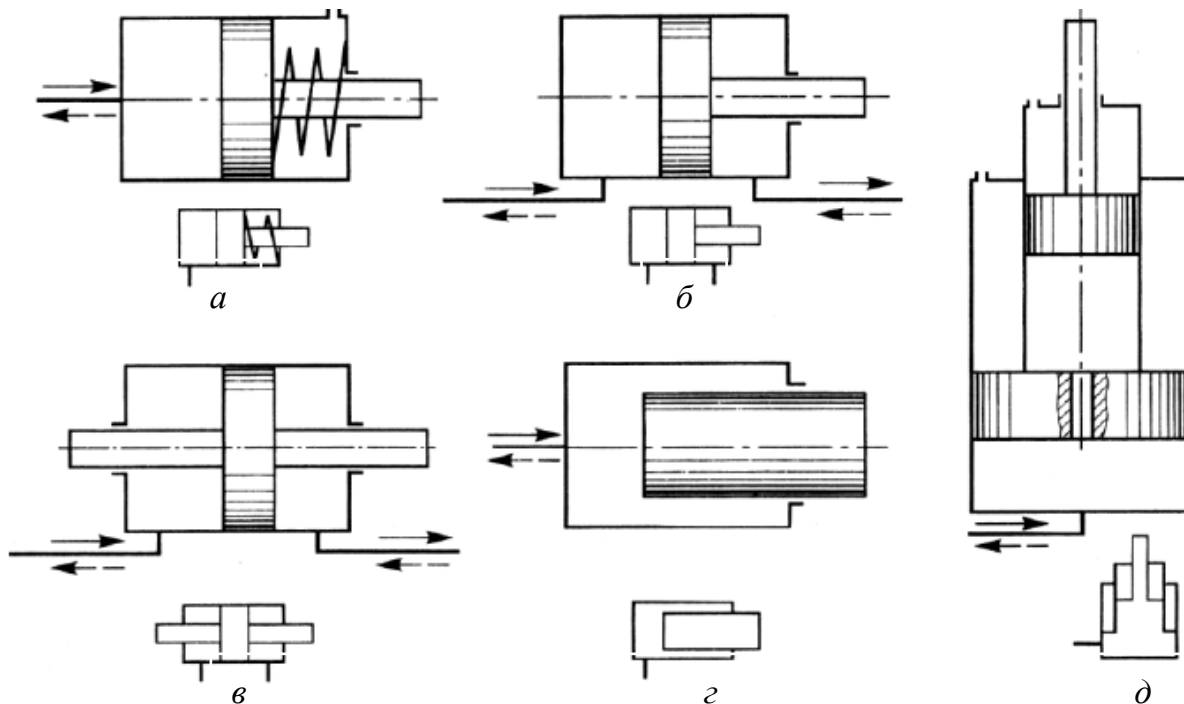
Схемы цилиндров и их условные обозначения:
